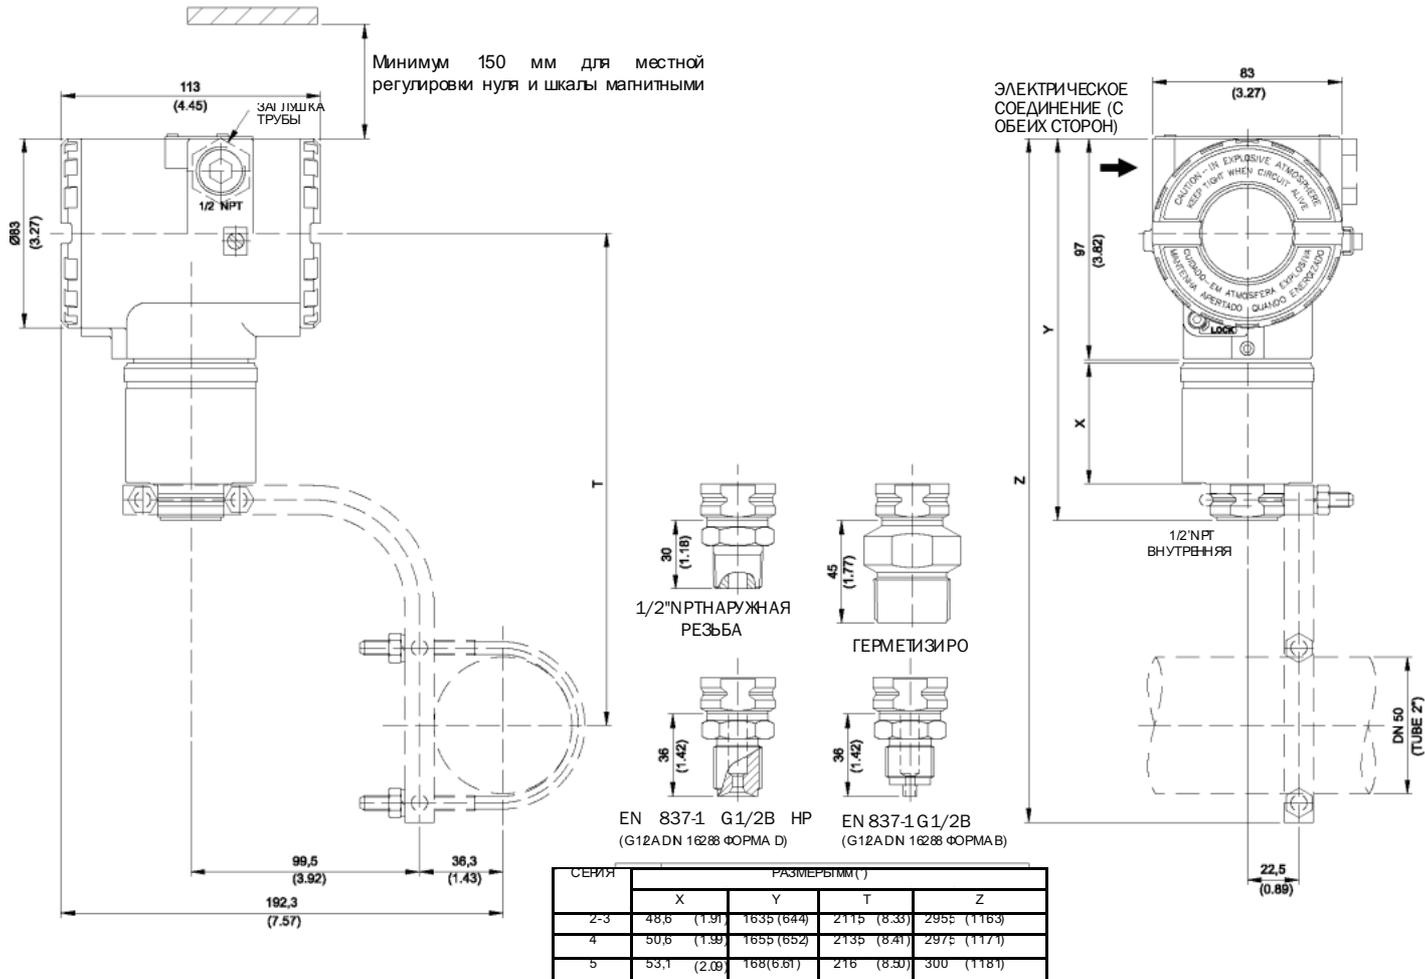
(а) – Размерный чертёж и положения установки для LD290
